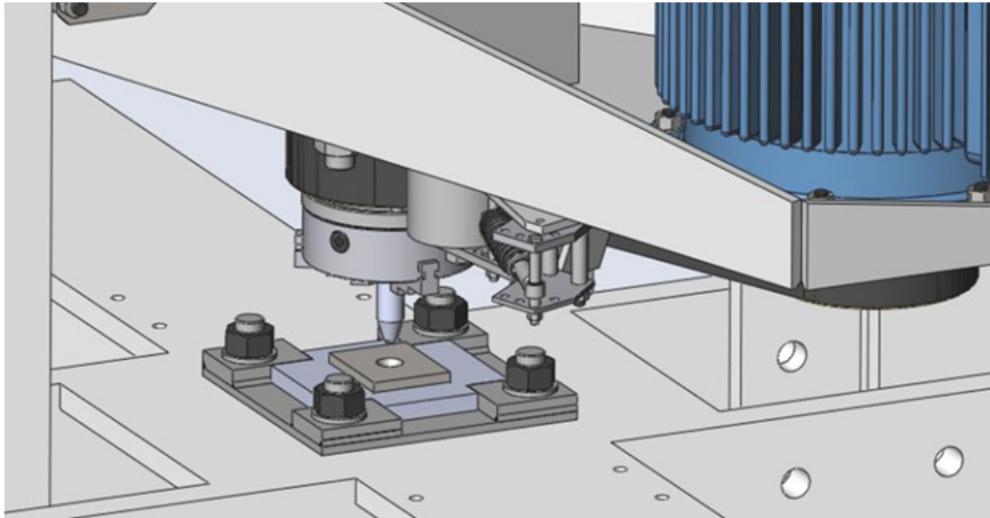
Sistema de fixação da base e do pino para a soldagem.
